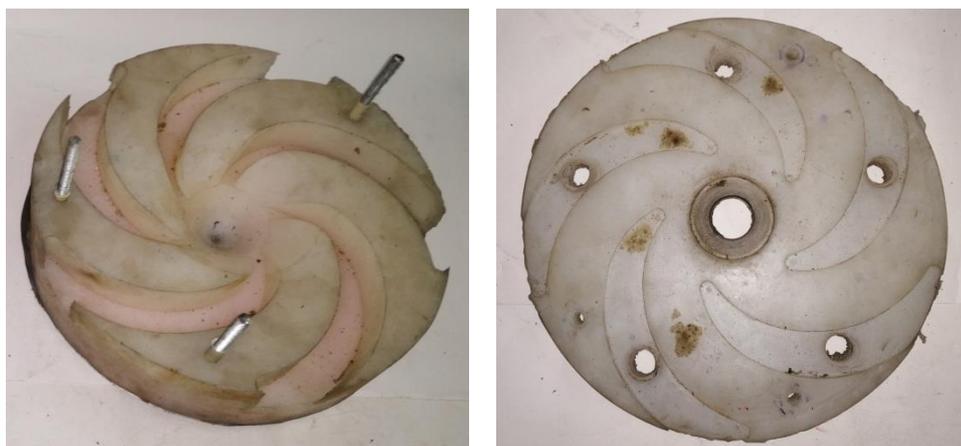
Отливки форм рабочего колеса из литейного силикона
